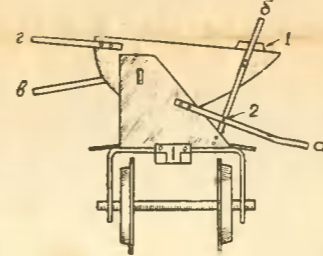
Вагонетка с механизмом подъёма и сбрасывателя (вид сверху)
